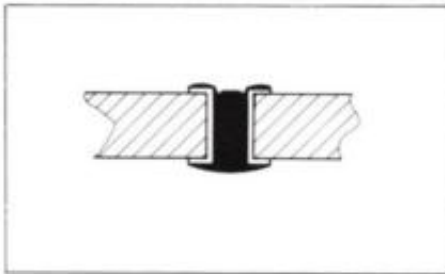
Belemmerde doorvloeit door slecht soldeerbare zones.
